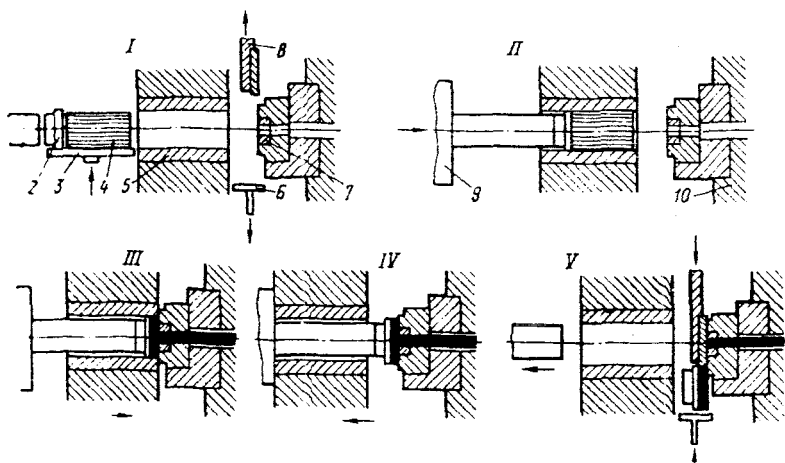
Схема прессования сплошных профилей: 1 - пресс-штемпель; 2 - пресс-шайба; 3 - устройство для подачи заготовок; 4 - заготовки; 5 - контейнер; 6 - приемник пресс-остатка; 7 - матрица; 8 - ножницы; 9 - прессующая траверса; 10 - передняя поперечина
